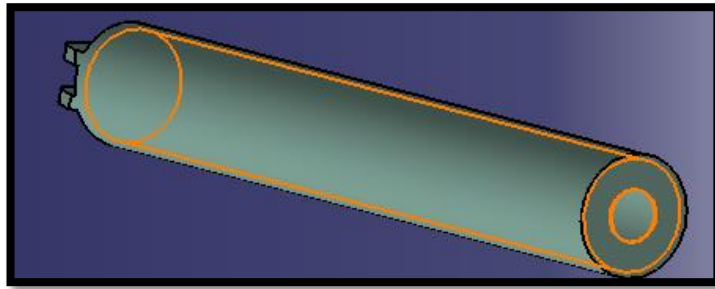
Seat mounting frame 11: Pocket.2 pieza 1 amortiguador
